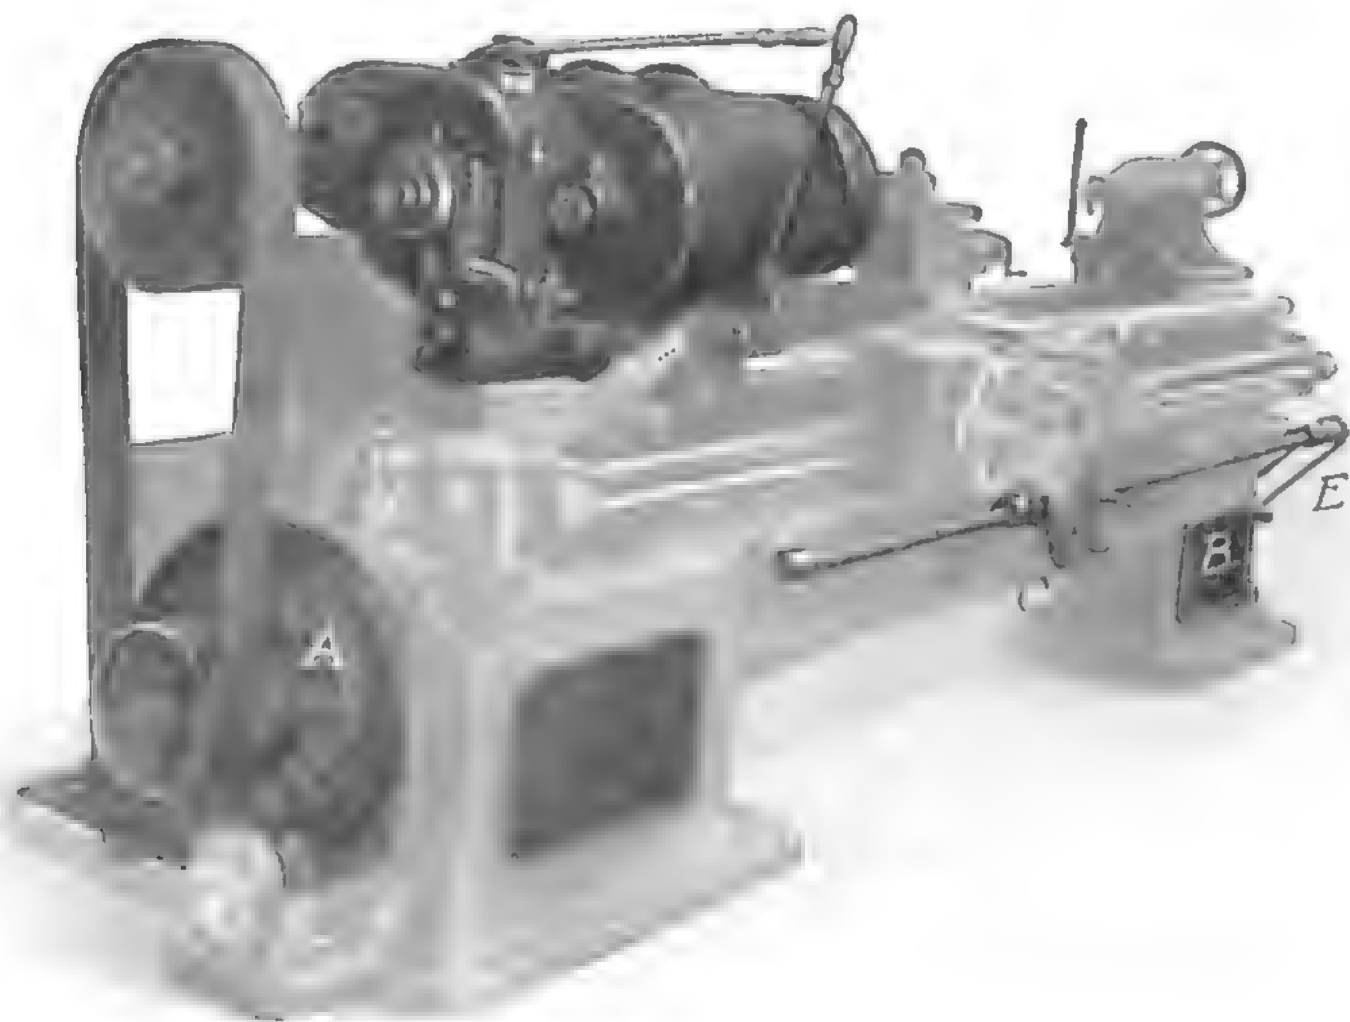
Schnelldrehbank mit Reguliermotor (A), Regulier-Anlasser (B), Handrad (C), Welle (D), Kette (E) zur Betätigung des Anlassers.
